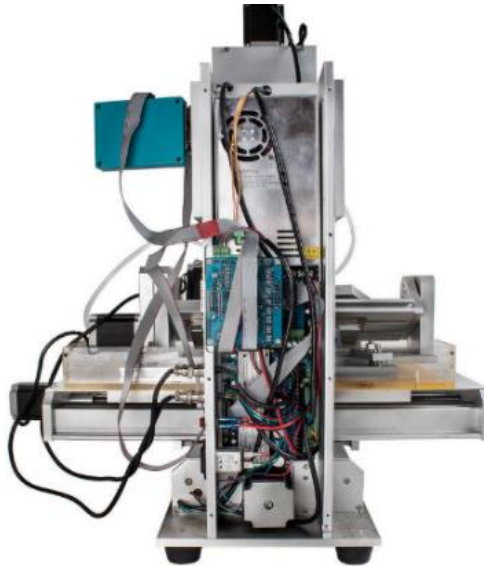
Máquina fresadora Router CNC 5 Ejes
